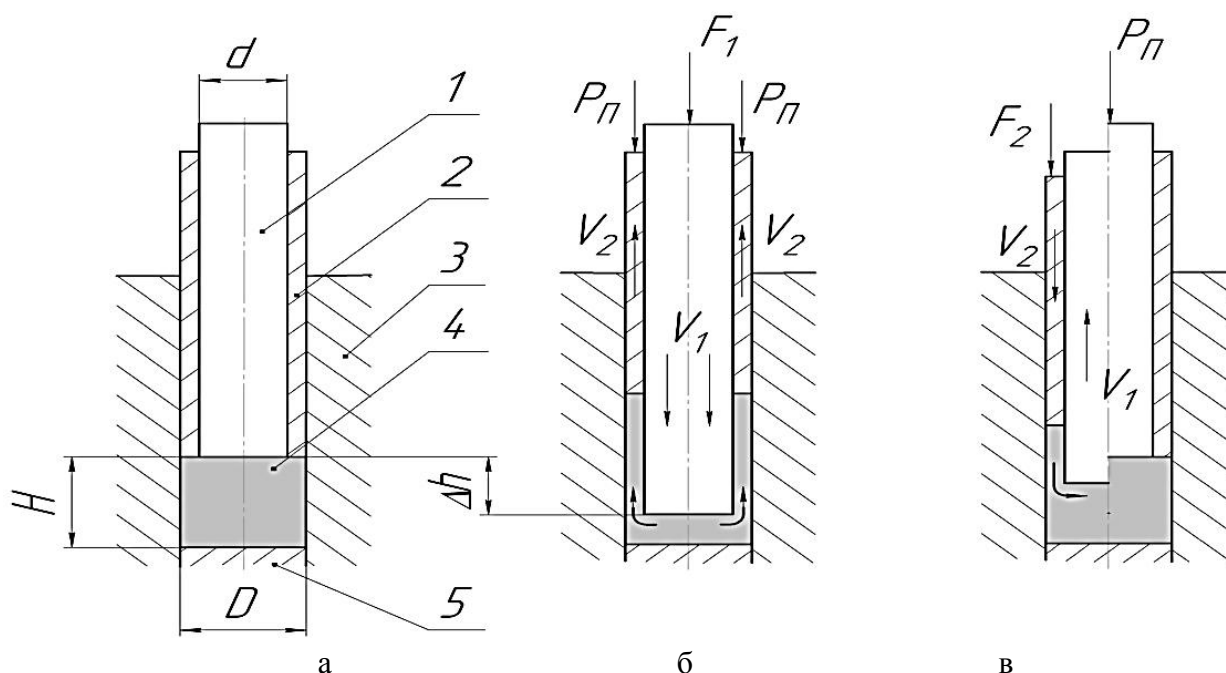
Схема обработки заготовки реверсивной закрытой прошивкой с противодавлением (1 – внутренний пуансон; 2 – внешний пуансон; 3 – штамп; 4 – заготовка; 5 – опора):
